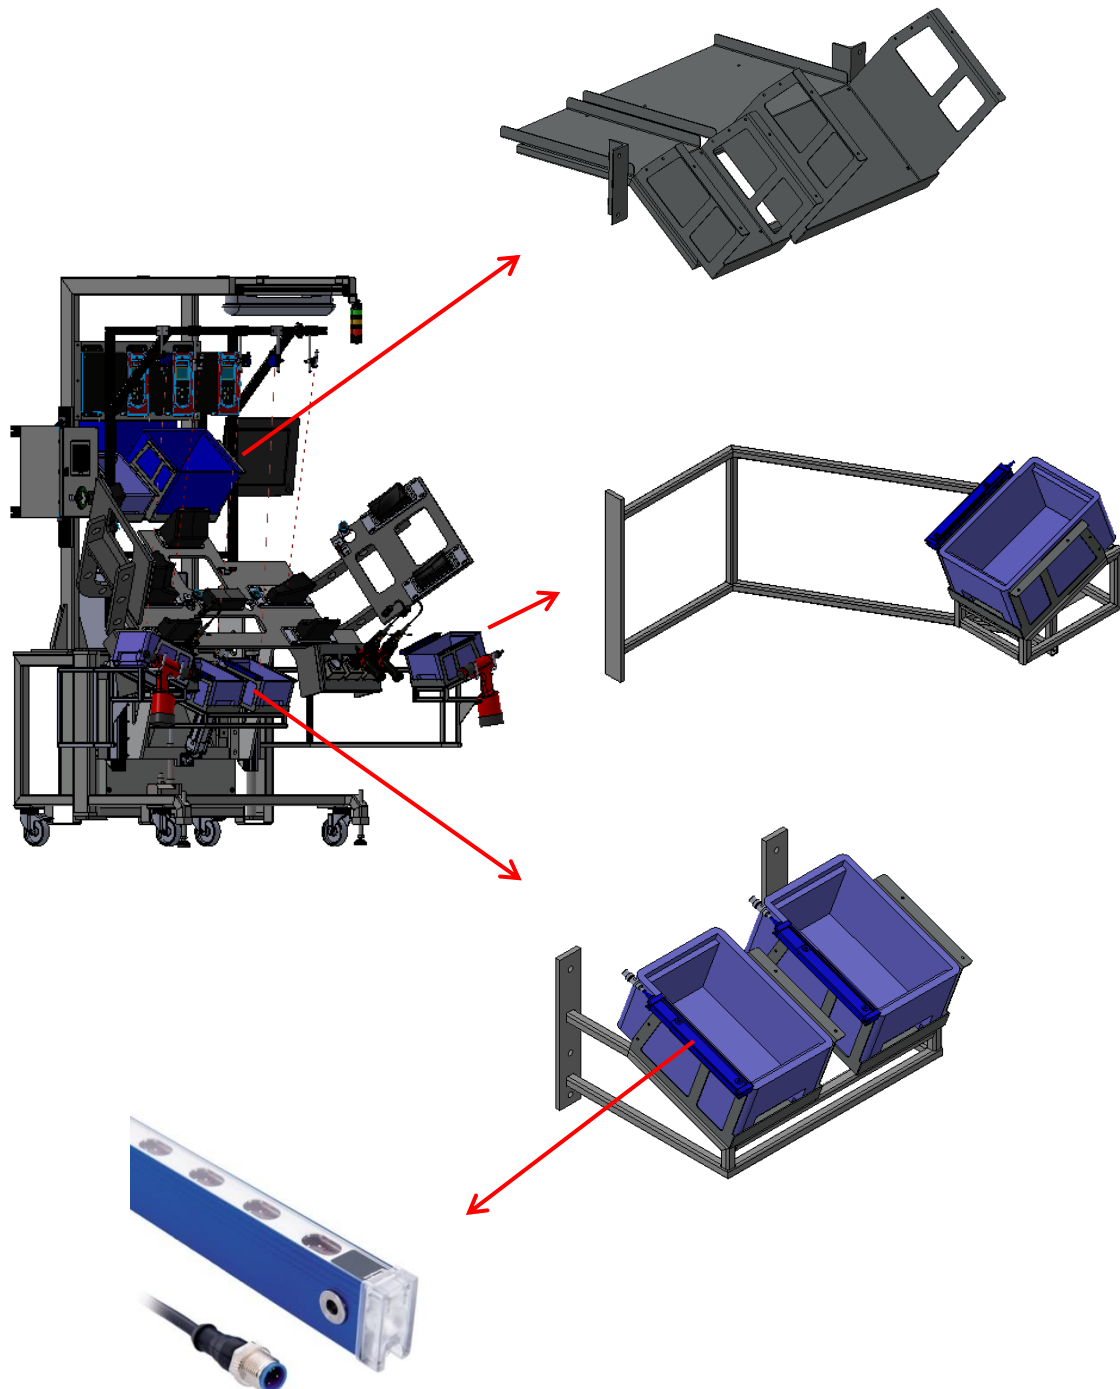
Estructuras para cajones con sistema Pick to light FS13
